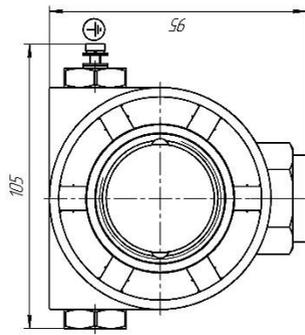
Общий вид сигнализатора уровня с присоединительной резьбой G1.1/2"
